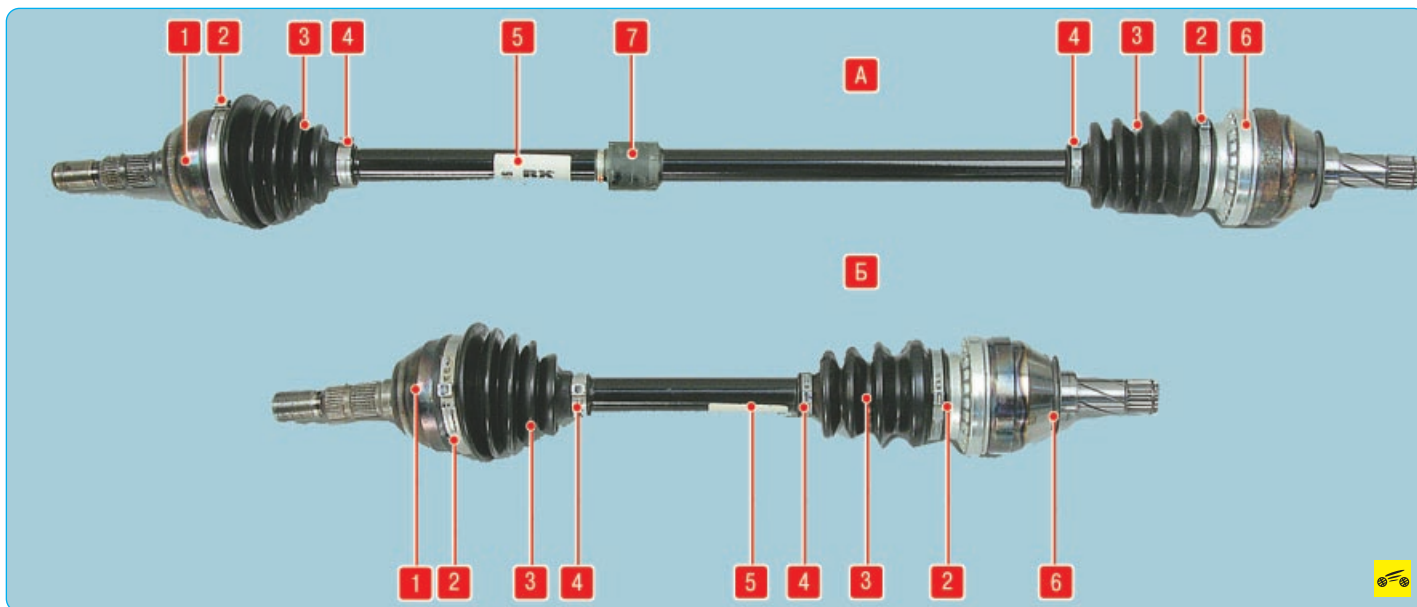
Приводы передних колес: А — привод правого переднего колеса; Б — привод левого переднего колеса: 1 — наружные шарниры равных угловых скоростей; 2 — большие хомуты крепления чехлов шарниров; 3 — чехлы шарниров; 4 — малые хомуты крепления чехлов шарниров; 5 — валы приводов; 6 — внутренние шарниры равных угловых скоростей; 7 — демпфер крутильных колебаний
